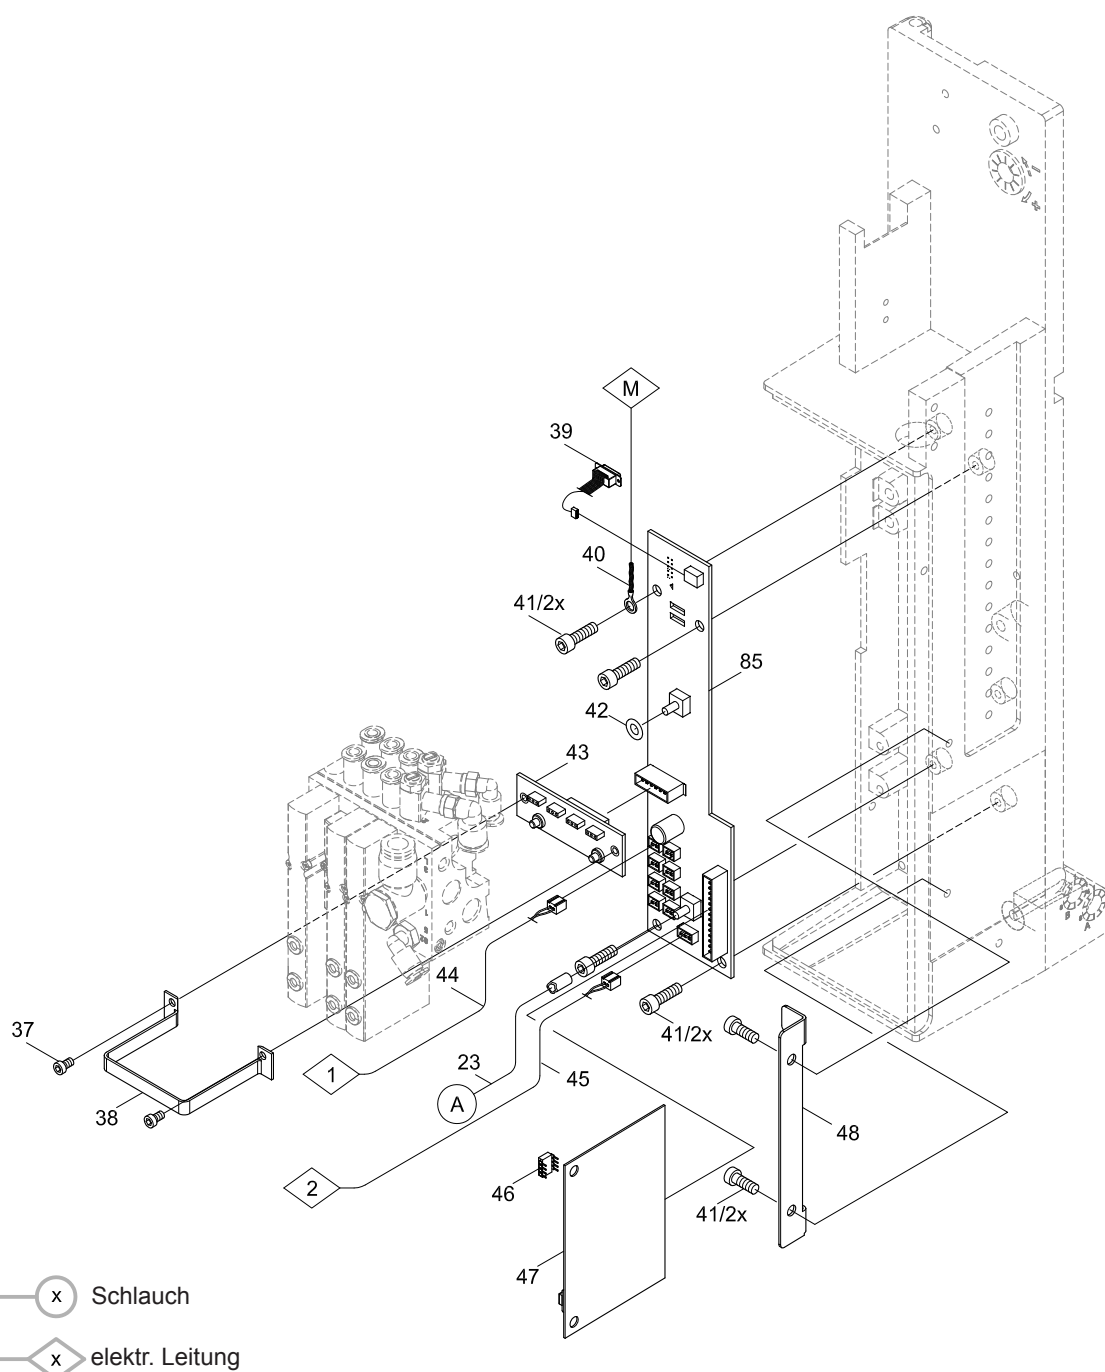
Elektronik Trägerbaugruppe - Ersatzteil
